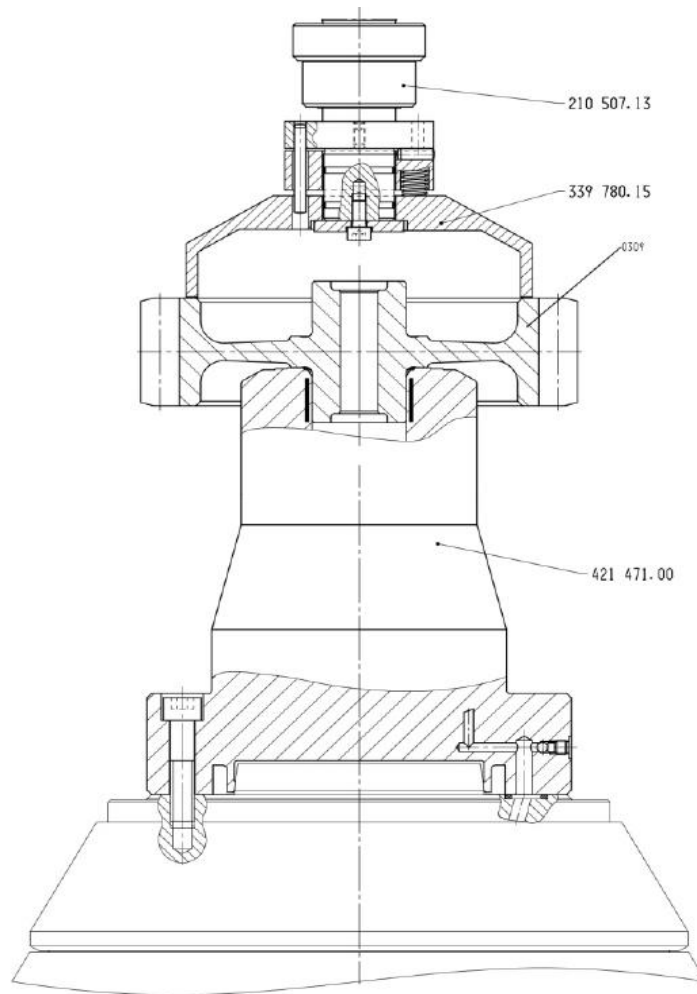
Гидравлическое приспособление для зажима зубчатого колеса
